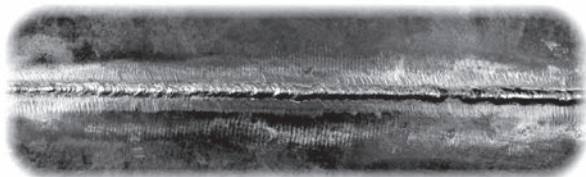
Кореневий шов зі зворотного боку зварного стикового з'єднання, виконаного на вертикалі
